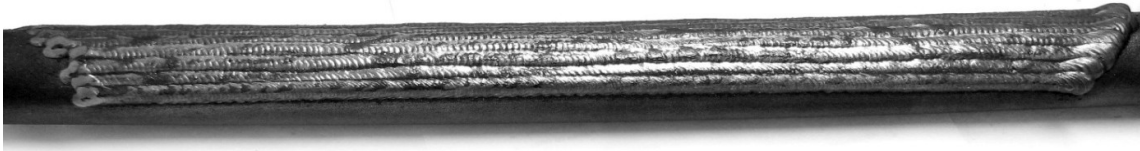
Corpo de prova com deformação, soldado na posição plana
